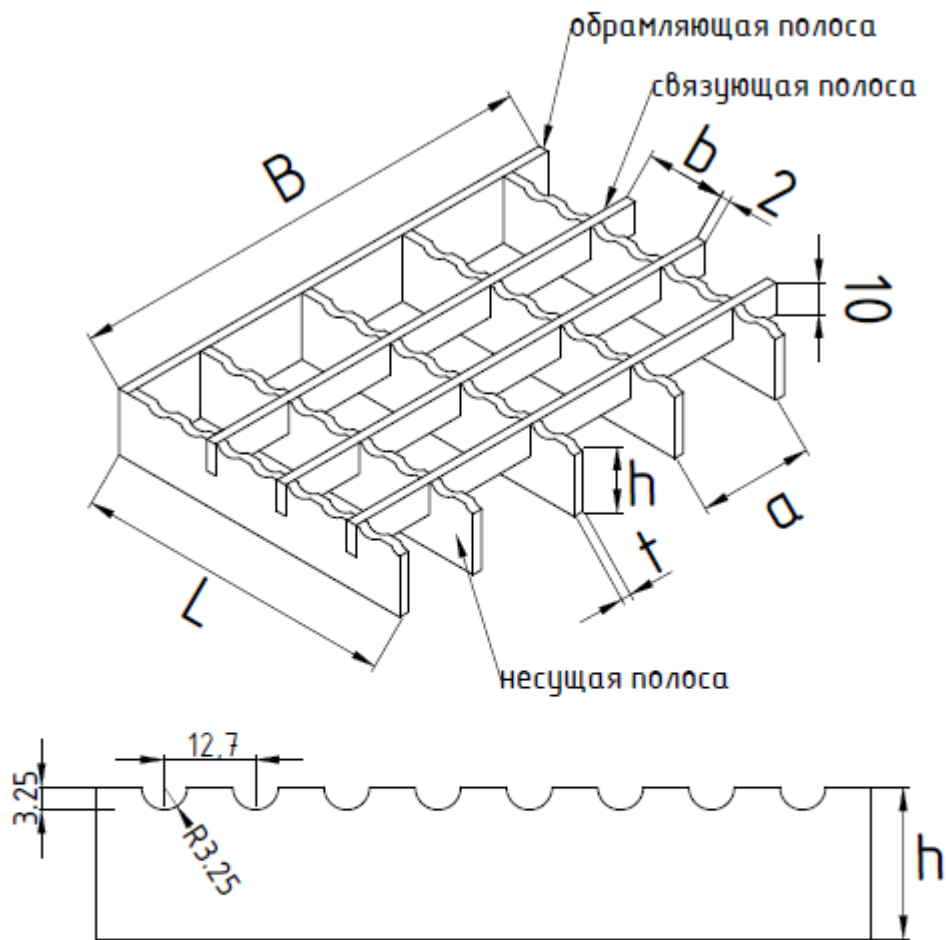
Схема сварного настила с противоскольжением
